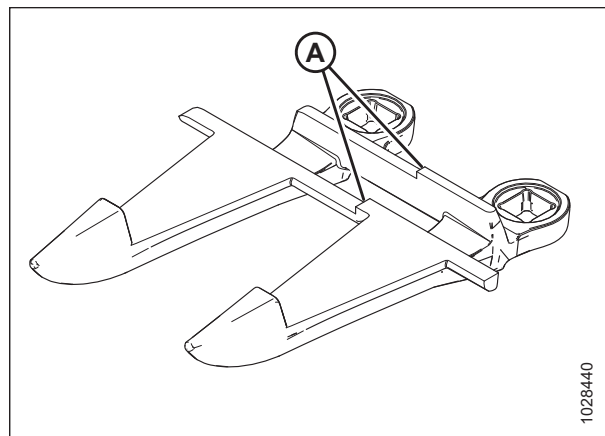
Загострений центральний протиріжучий палець ножа
